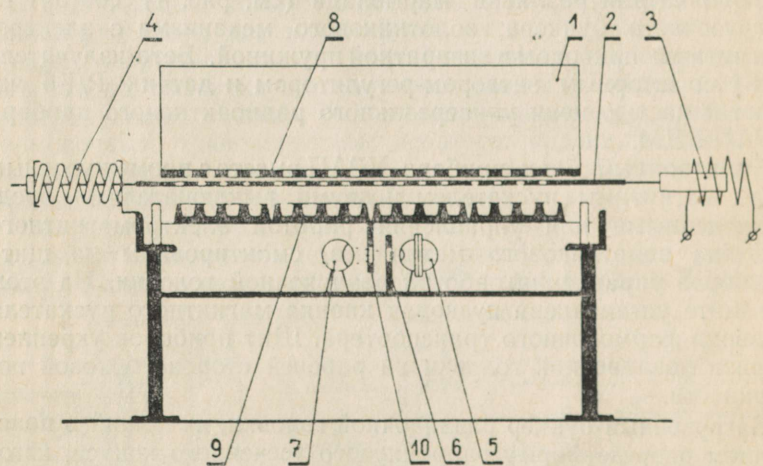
РАЗЛИВОЧНАЯ ГОЛОВКА МАРМЕЛАДО-РАЗЛИВОЧНОЙ МАШИНЫ:
